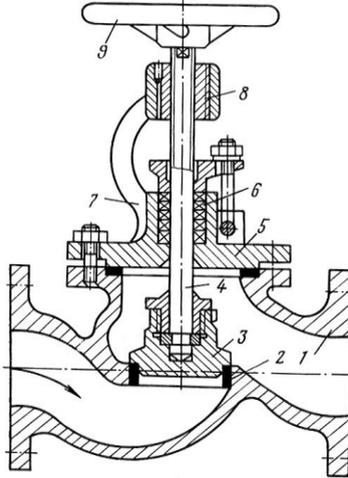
Клапан (вентиль) проходной: 1- корпус; 2- уплотнительное кольцо; 3- золотник; 4- шток; 5- крышка; 6- сальник; 7- стойка; 8- ходовая гайка; 9- маховик.
